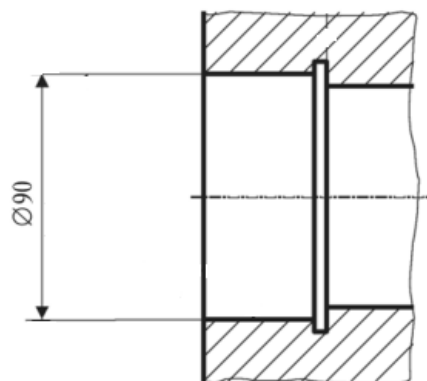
Цилиндрическая поверхность корпуса под установку подшипника
